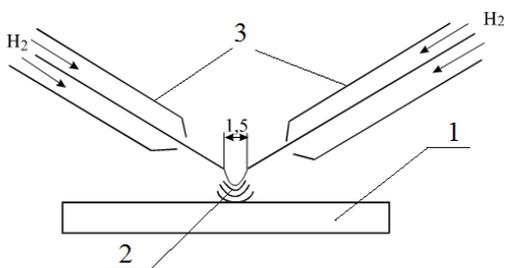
Схема процесса атомно-водородной сварки:
